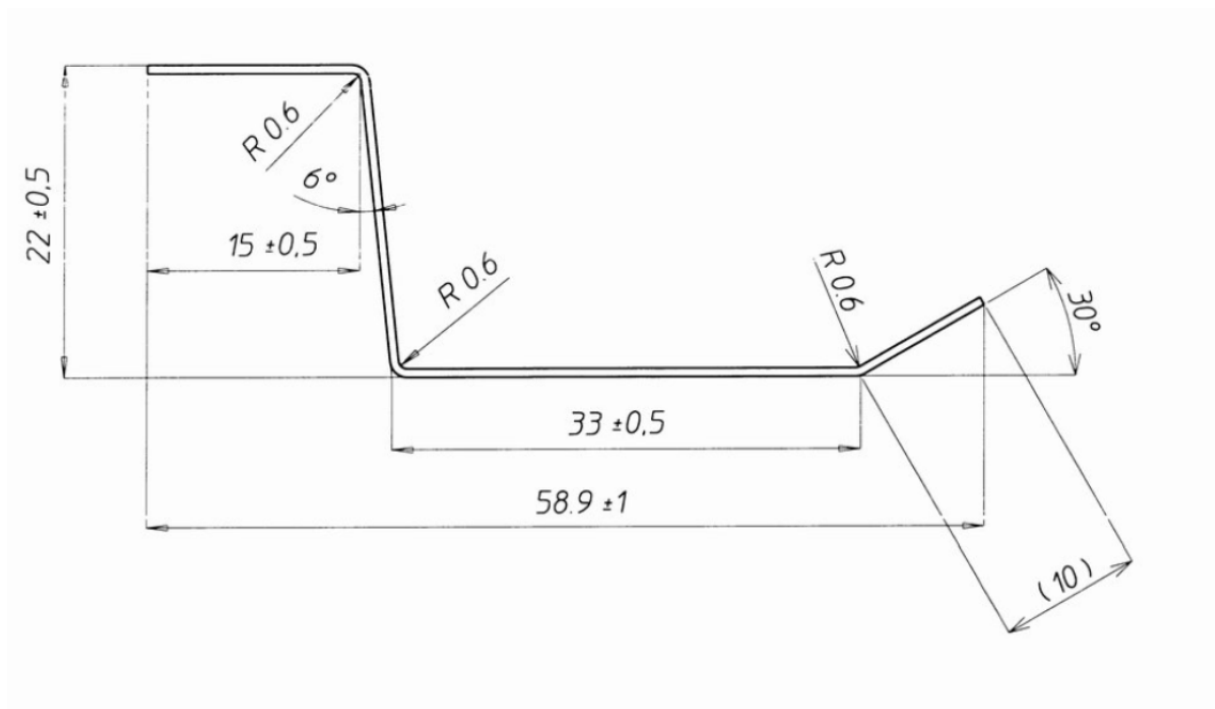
Section cotée du profilé Stil®TIL MOB 300
